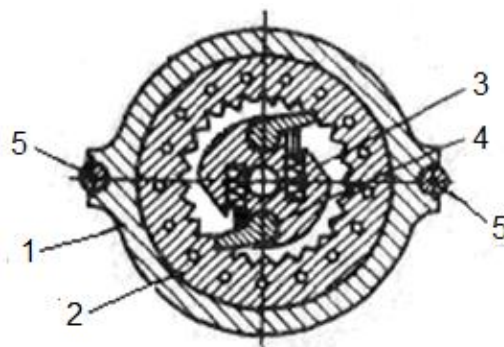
Поворотный механизм с двумя собачками в корпусе
